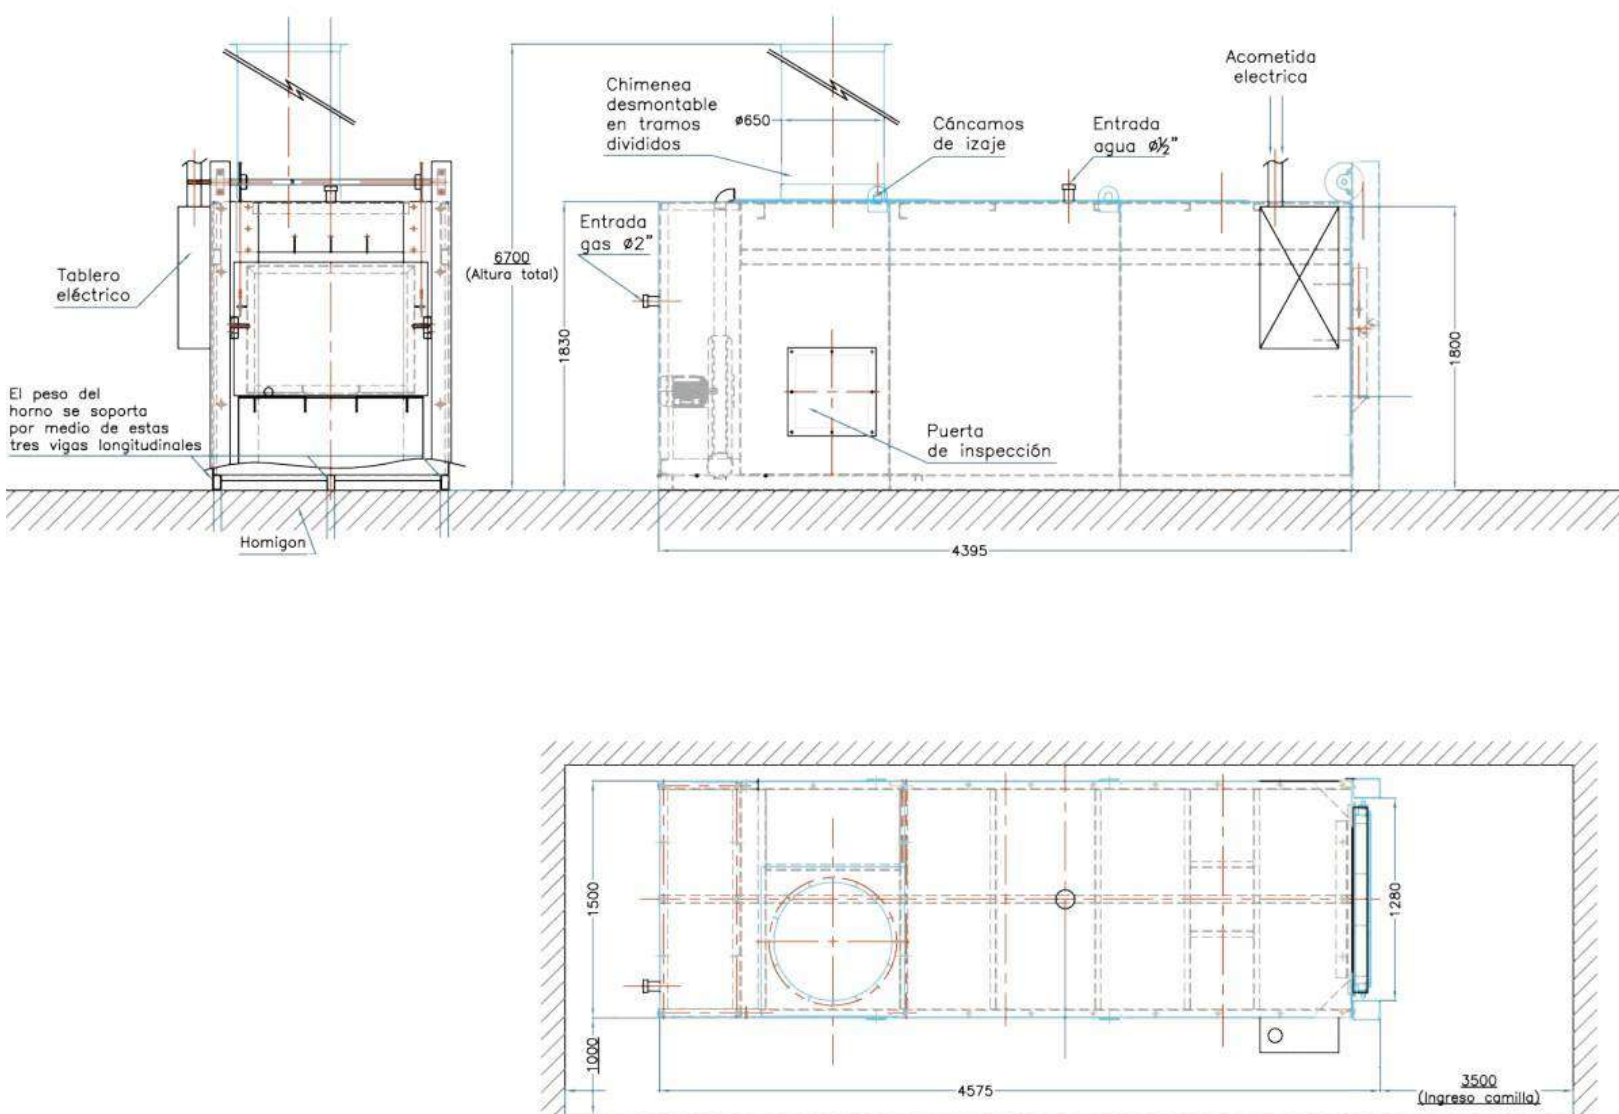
Planos con detalles constructivos del horno crematorio modelo Eco Plus Burner Gas. (CALTEC, 2021)
